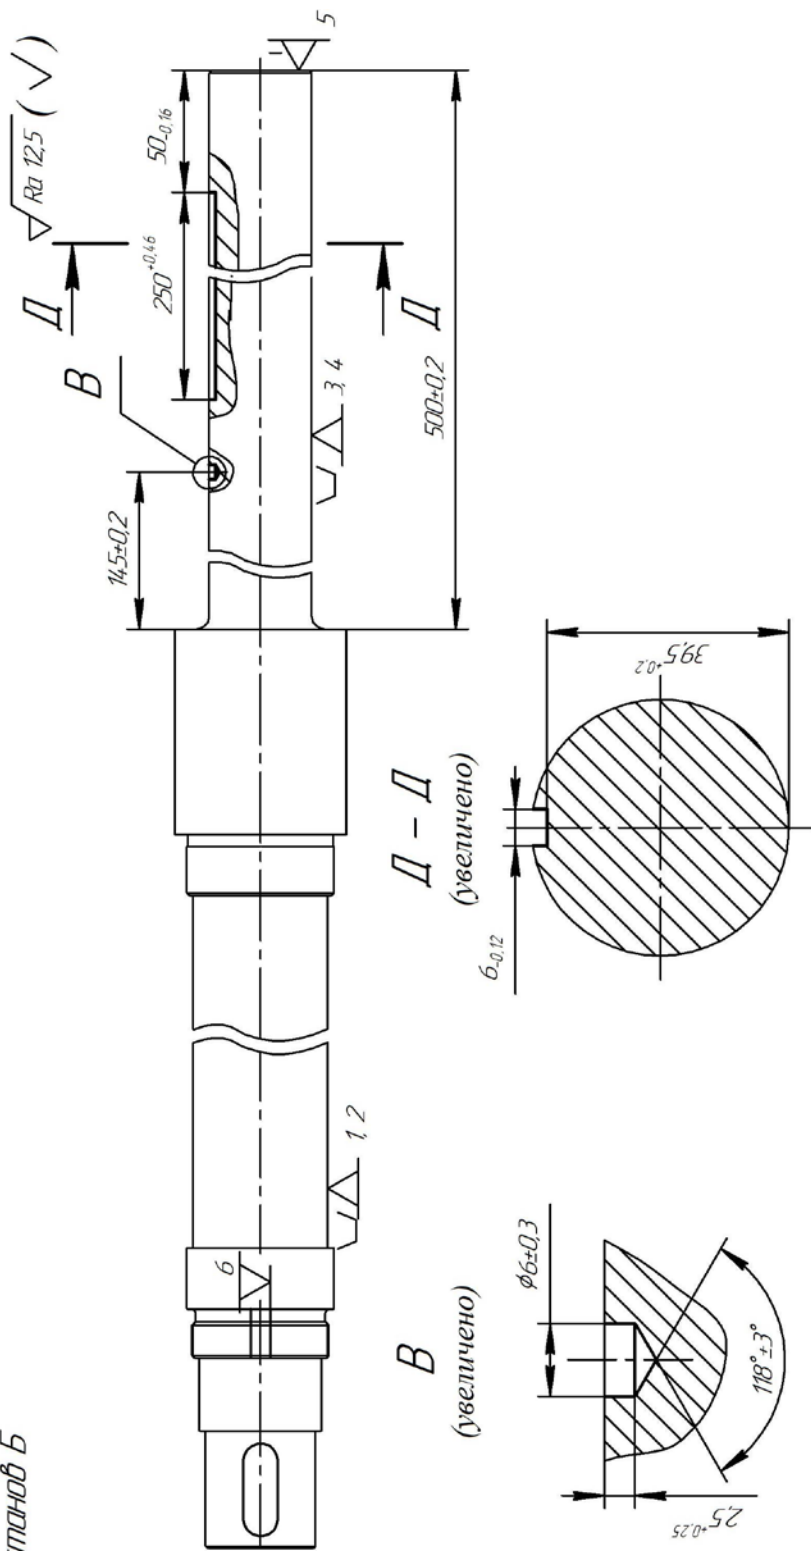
Схема базування заготовки на операції фрезерній 030, установ Б
